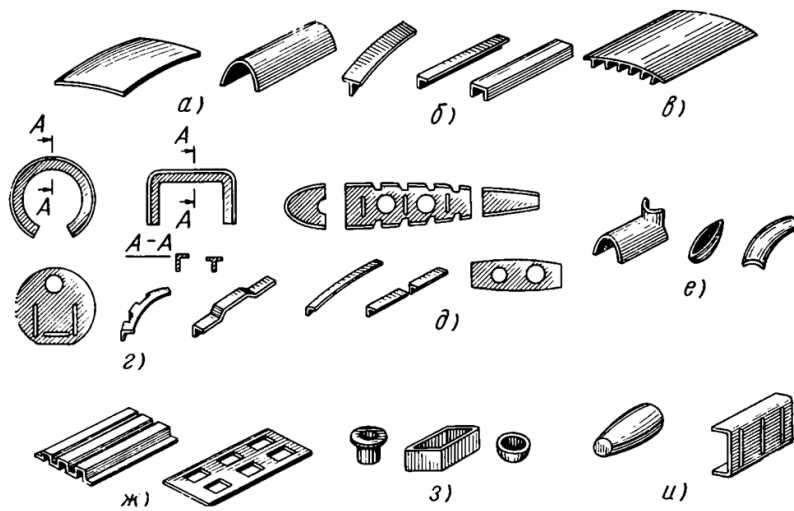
Типові деталі, що виготовляються штампуванням з листових профільованих та трубчастих напівфабрикатів: а - обшивки; б - стрінгери; в - монолітні панелі; г - деталі шпангоутів; д – деталі нервюр; е - залізи, закінцювання; ж - гофри, панелі; з – деталі внутрішнього набору; і - обичайки та перегородки (А.Л.Абібов / Технологія літакобудування)
